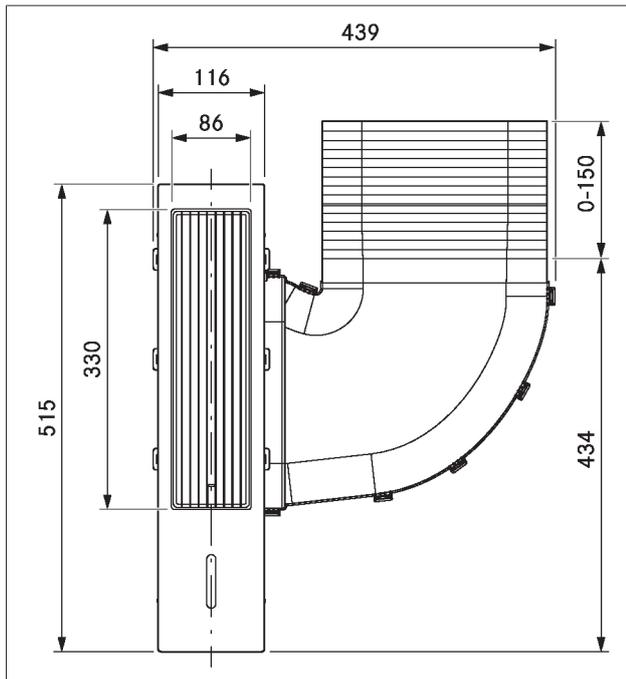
CKA2/CKA2AB Gerätemaße Draufsicht
